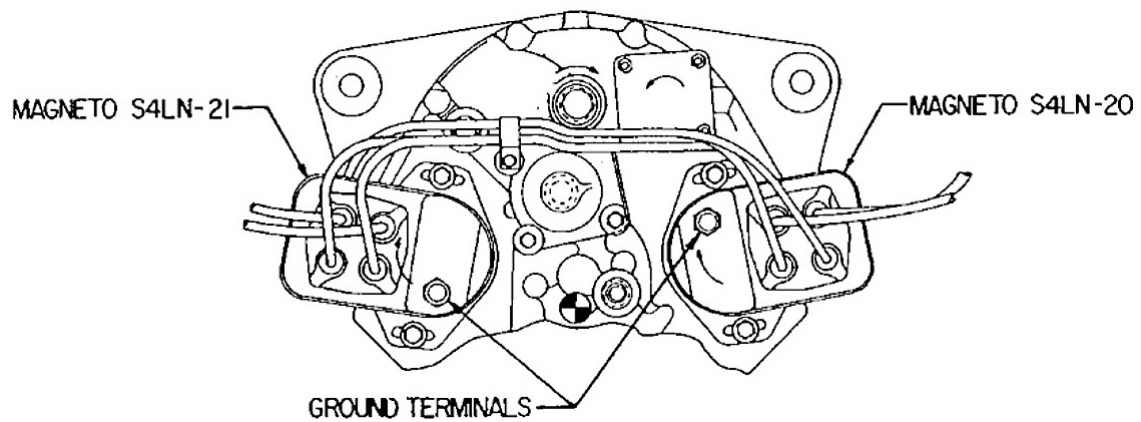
Esquema de montaje de magnetos en motor Lycoming O-435
